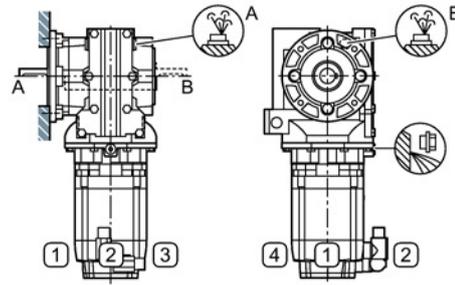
Einbaulagen für Stirnradschneckengetriebe C, Fußausführung, Baugrößen 39 - 89, 2-stufig
